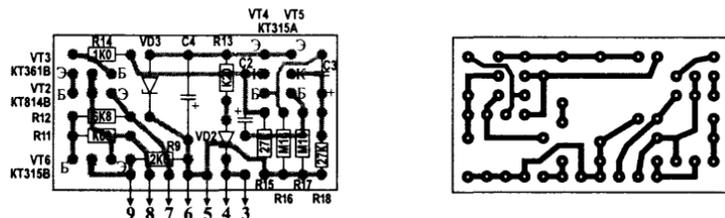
Монтажная плата схемы замещения (Блок А) микросхемы К224ГТ2 для реле поворотов 23.3747 (масштаб 1:1).
